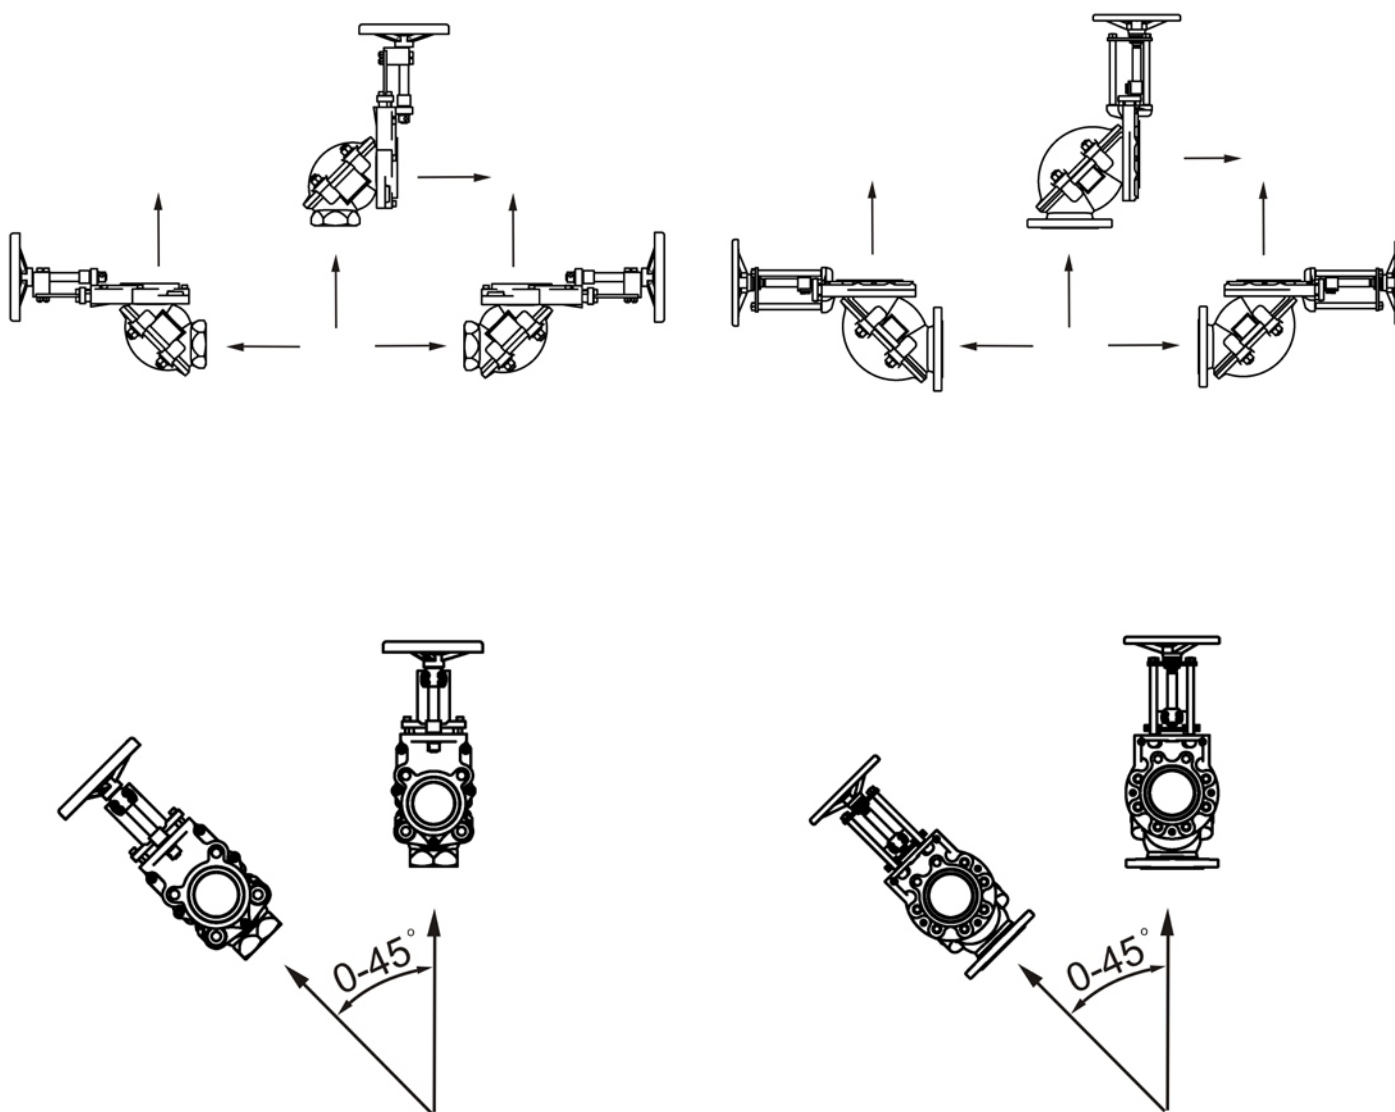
Установка обратных коленных клапанов с ножевой задвижкой(нач. с левой стороны) типа COMBI 01 и COMBI 11
